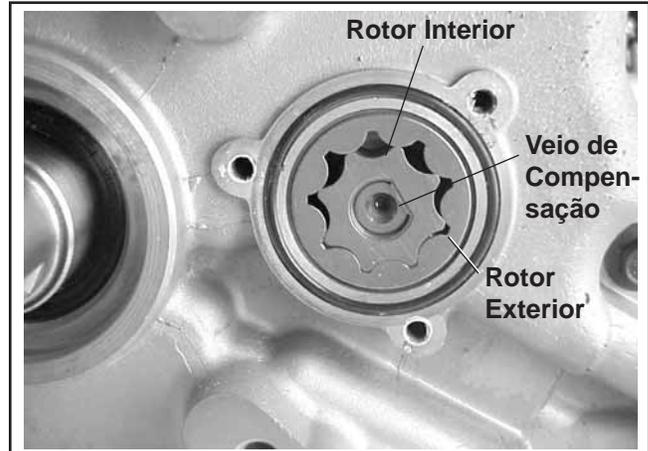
Instalar as Engrenagens da Bomba do Óleo e o O-Ring.
